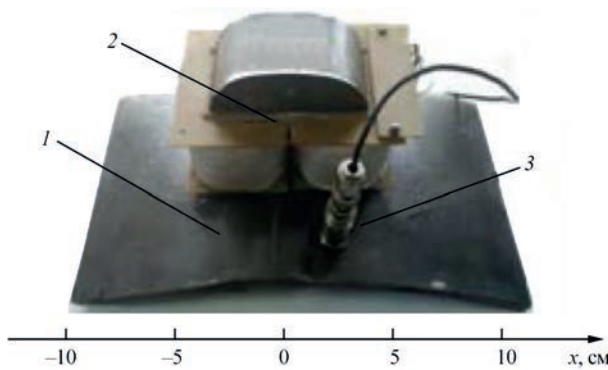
Розташування НЕМ на фрагменті труби з повздовжнім зварним з'єднанням: 1 – фрагмент труби; 2 – НЕМ; 3 – перетворювач акустичної емісії
